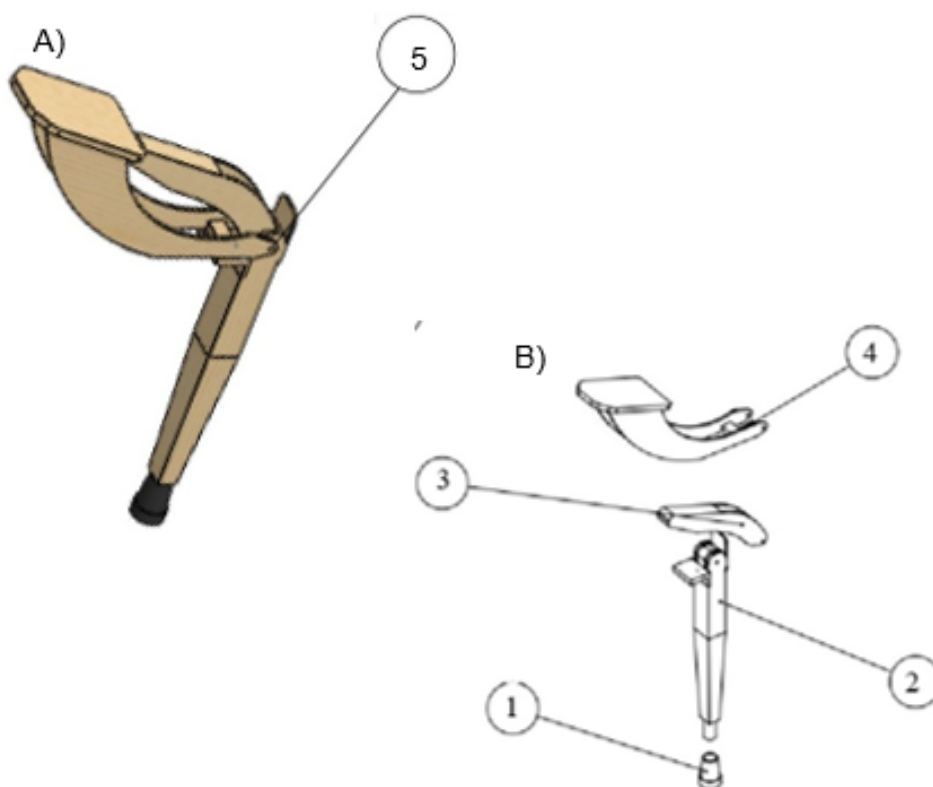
a) Prototipo terminado. b) Ensamblaje del prototipo.
